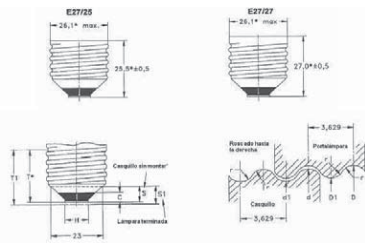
Dimensiones del casquillo de una bombilla en milímetros.
